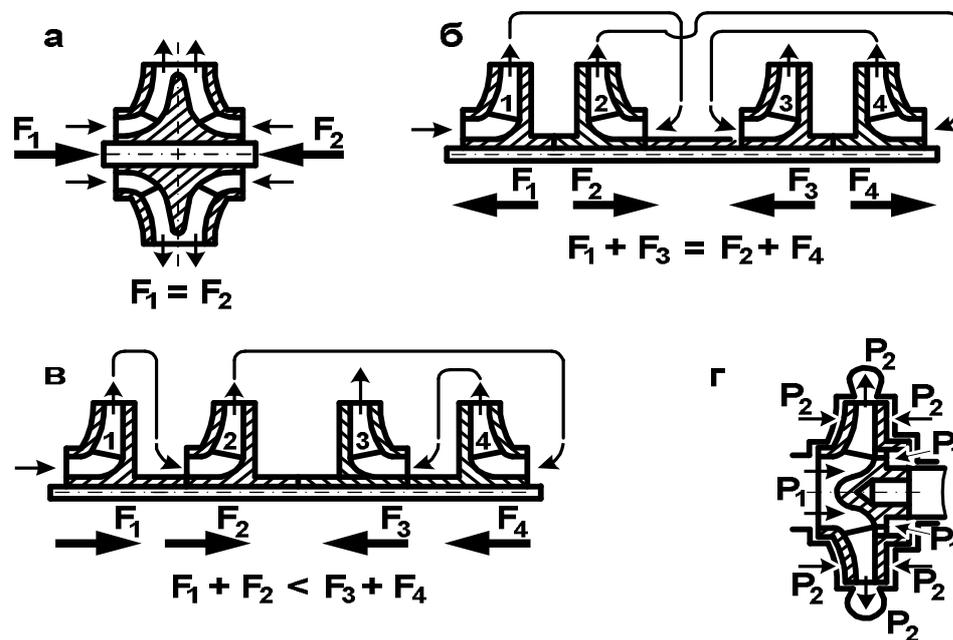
Способы уравнивания осевых усилий: а – применение рабочих колес с двухсторонним подводом жидкости; б – встречное парное расположение рабочих колес; в – встречное групповое расположение рабочих колес; г – применение разгрузочного отверстия в заднем диске рабочего колеса; F_1 , F_2 , F_3 и F_4 – осевое усилие на 1-е, 2-е, 3-е и 4-е колесо
